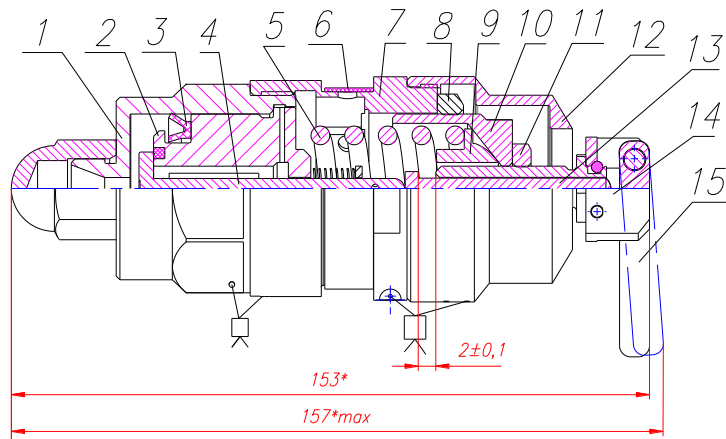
Предохранительный клапан КПП – (3-10): 1 - штуцер, 2 - седло, 3 - манжета, 4 - клапан, 5 - пружина, 6 - кольцо, 7 - корпус, 8 - контргайка крышки, 9 - опора, 10 - крышка, 11 - контргайка упора, 12 - колпак, 13 - толкатель, 14 - упор, 15 - рычаг.
